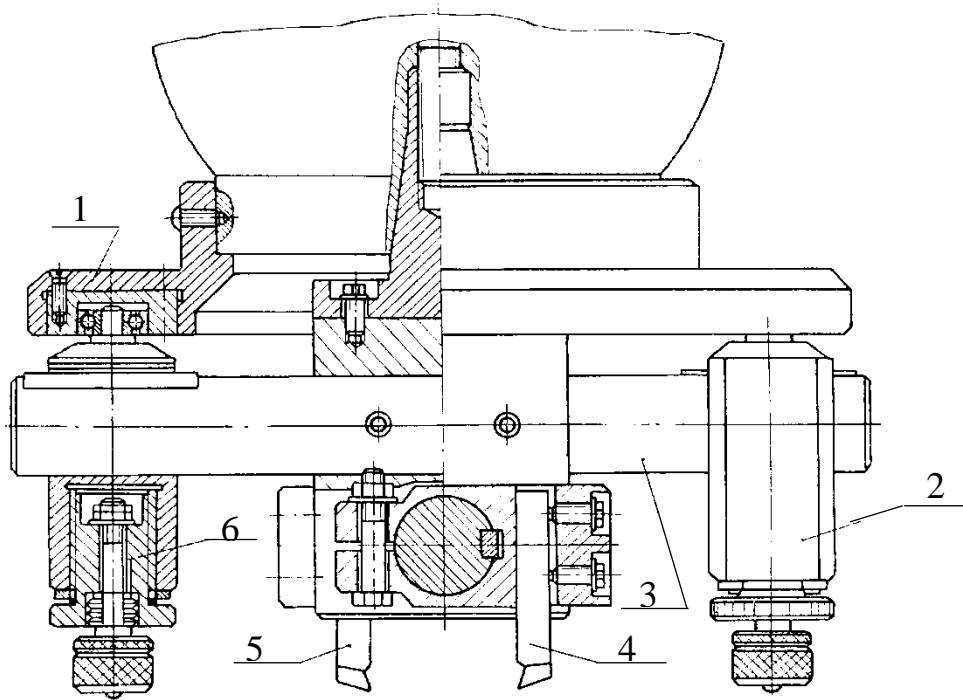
Фреза комбінована з вигладжувальними інденторами
